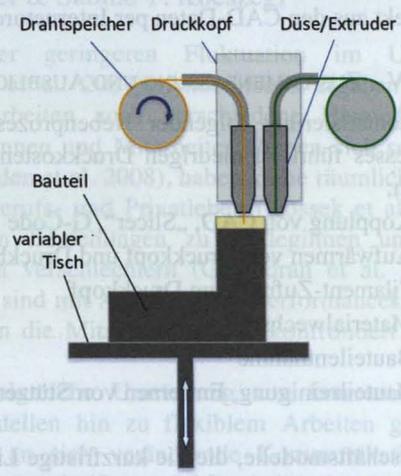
Fused Filament Fabrication Prinzip mit zwei Drahtrollen
